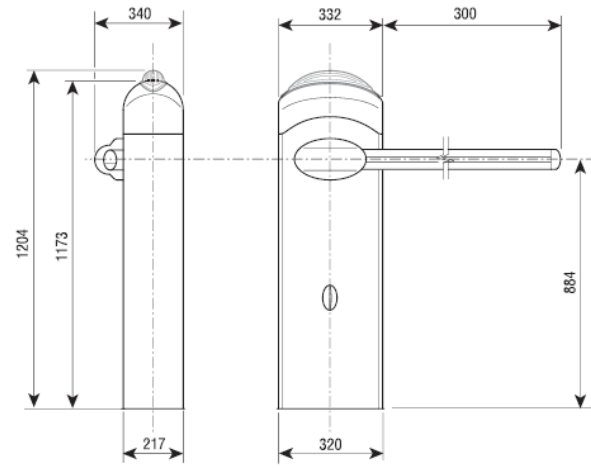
Detaje dhe ilustrim i barrierës së parkingut
